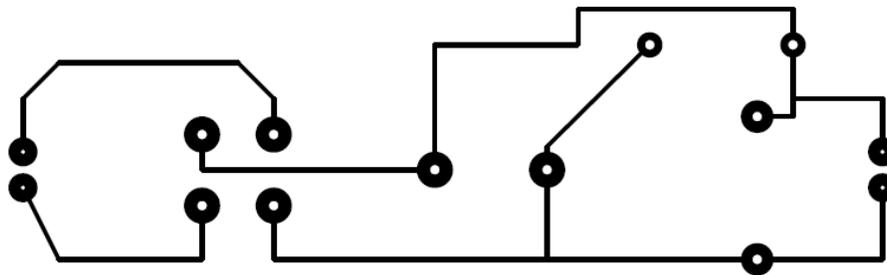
11. Circuito impreso de la fuente de voltaje
